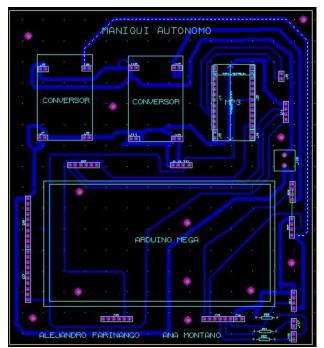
Esquemático PCB distribución de componentes. Elaborado por: Autores del proyecto
